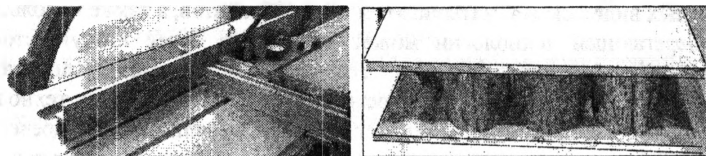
Изготовление торцового наполнителя на станке и склеенный щит
